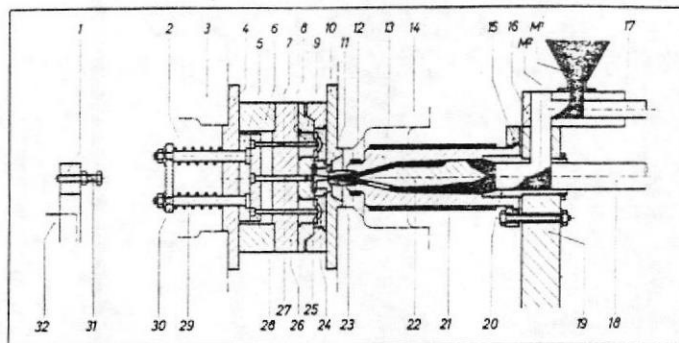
Esquema del proceso de inyección: «primer ciclo de trabajo». El molde ha sido cerrado por la unidad de cierre de la máquina.
